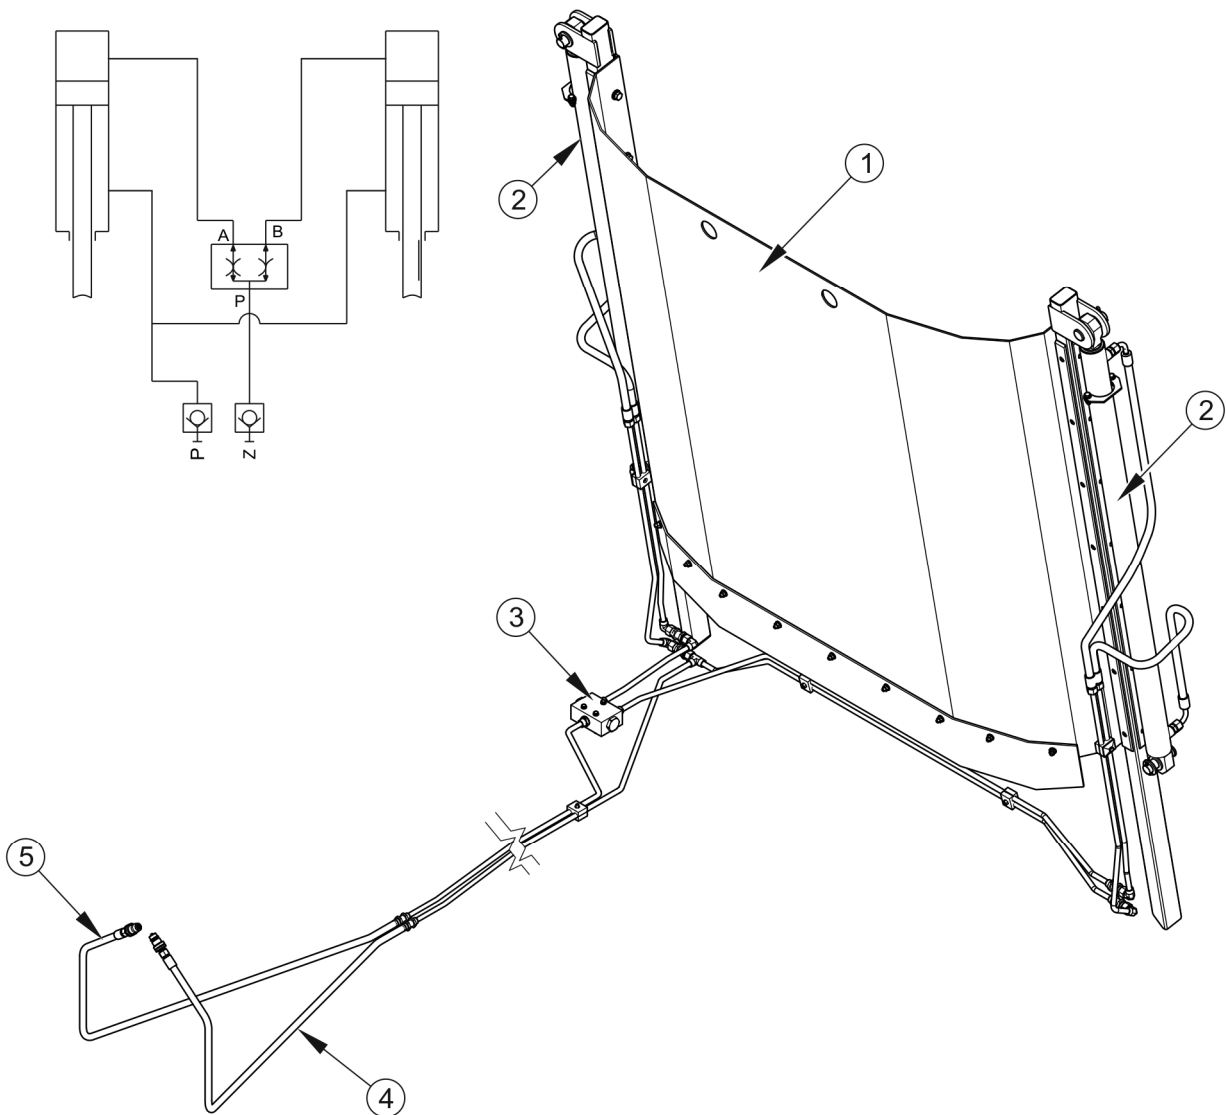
Construction et schéma de l'installation hydraulique de verrou
